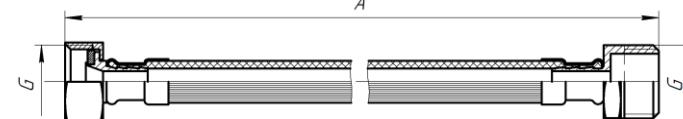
Габаритные и присоединительные размеры подводки вн-нар
